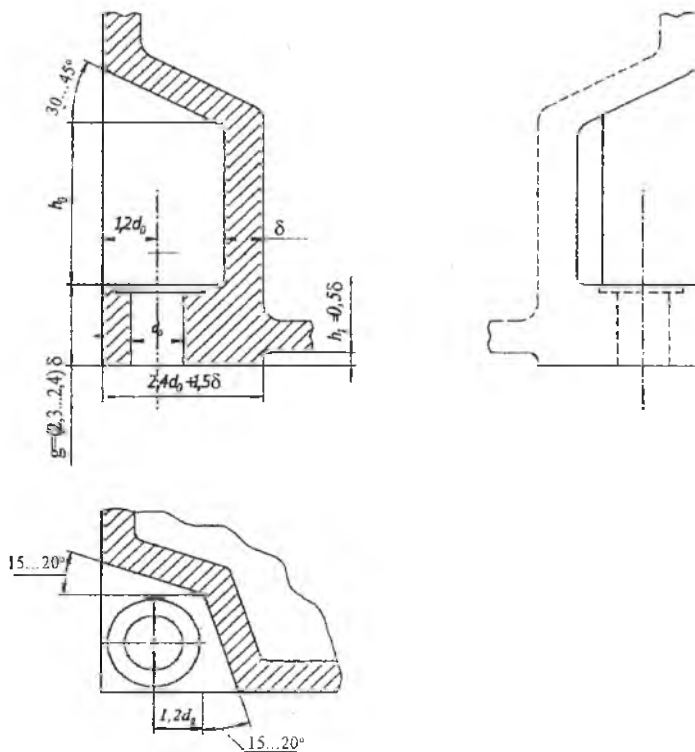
Узел крепления корпуса к основанию на углу корпуса
